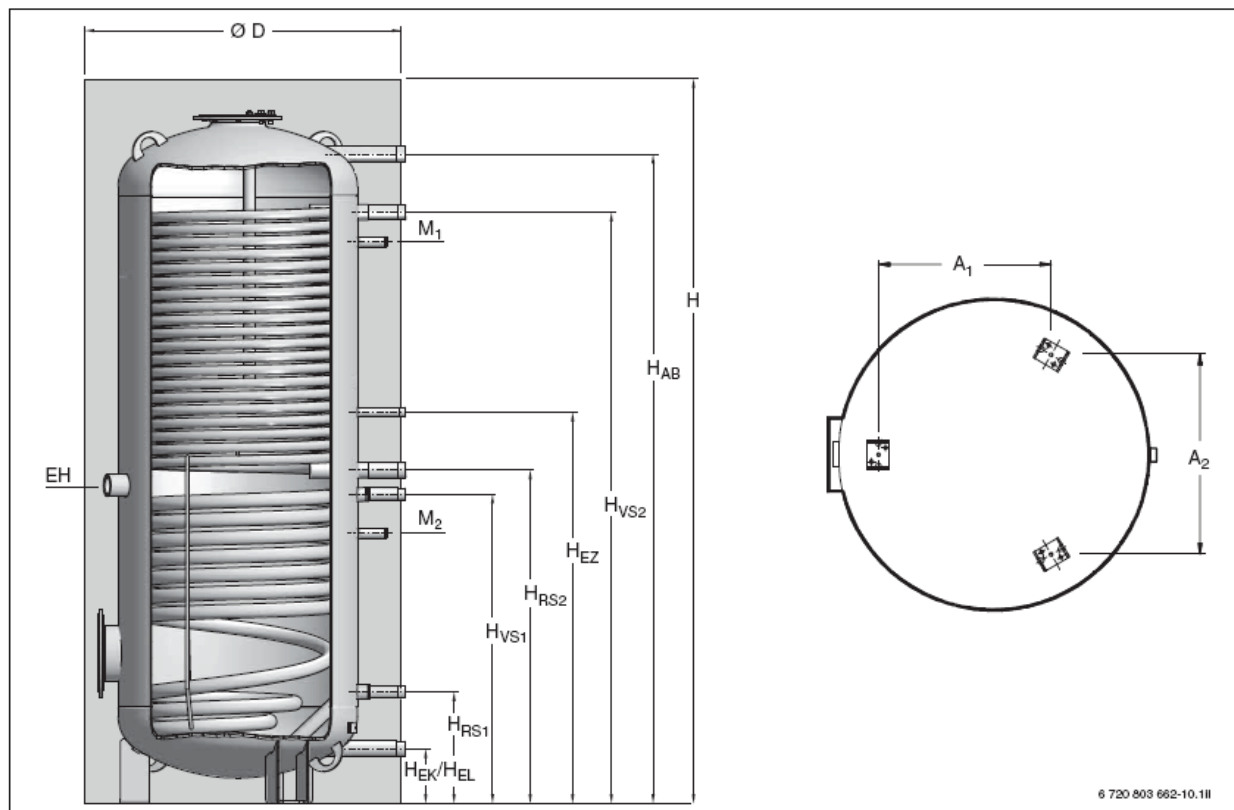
Габаритные размеры бивалентных баков-водонагревателей SMH400 EW и SMH500 EW
